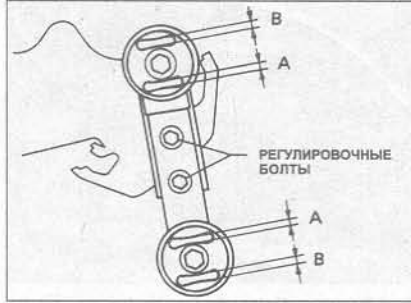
Регулировка задней под-установки двигатель/трансмиссия (Глава 10)
